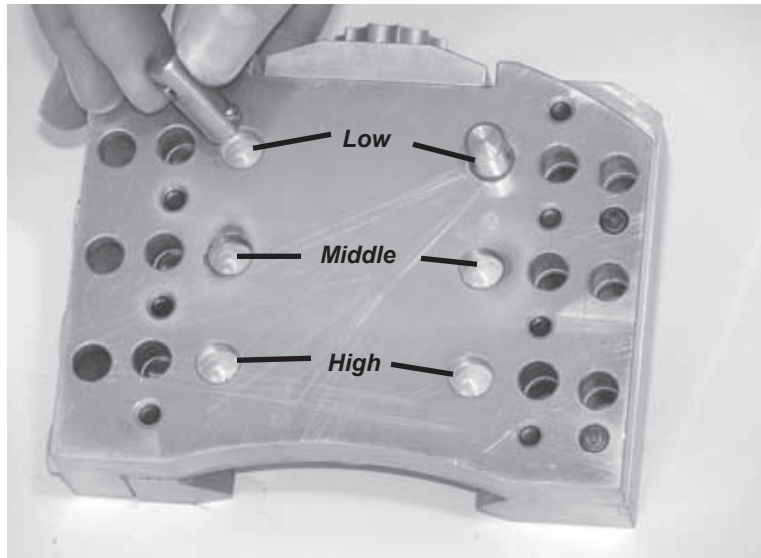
Inserte los pasadores guía de montaje en el portaherramientas.
